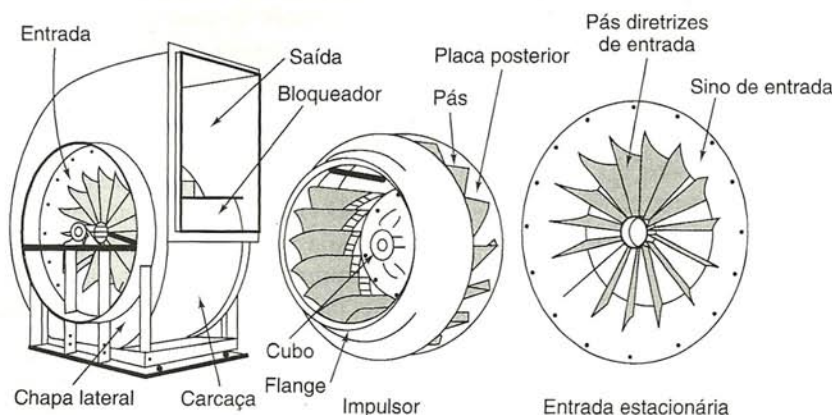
Vista explodida de um ventilador centrífugo típico [19].
